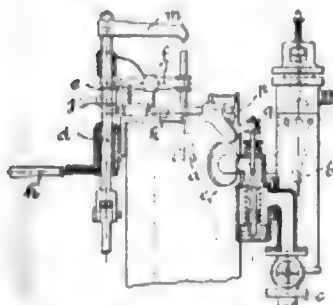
Anlassvorrichtung für Viertaktmaschinen.
